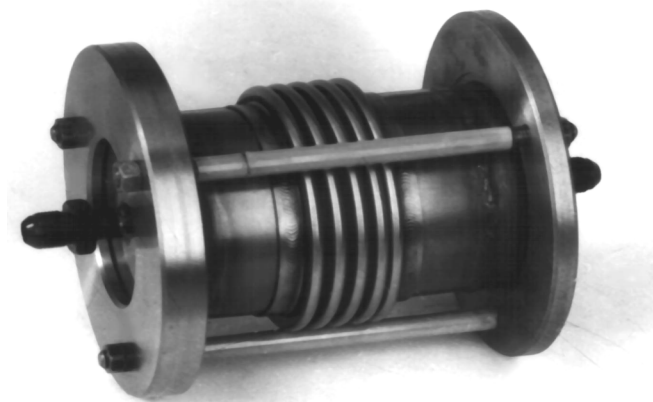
Натурный образец компенсаторов с приспособлением для испытаний на прочность до разрушения
